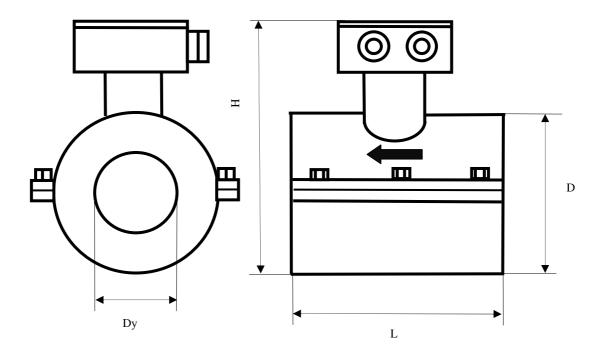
Габаритные размеры преобразователя ПРЭ -0114 модель 1
